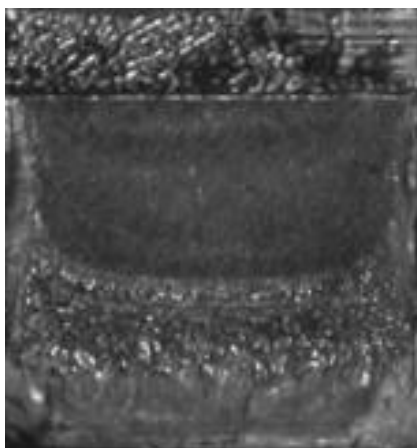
Photographie macro du faciès de rupture d'une éprouvette SENB impactée [8]
